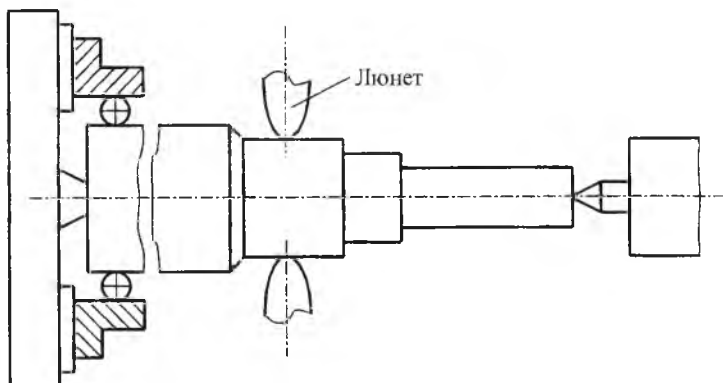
Схема обтачивания заготовки для полужесткой колонны
